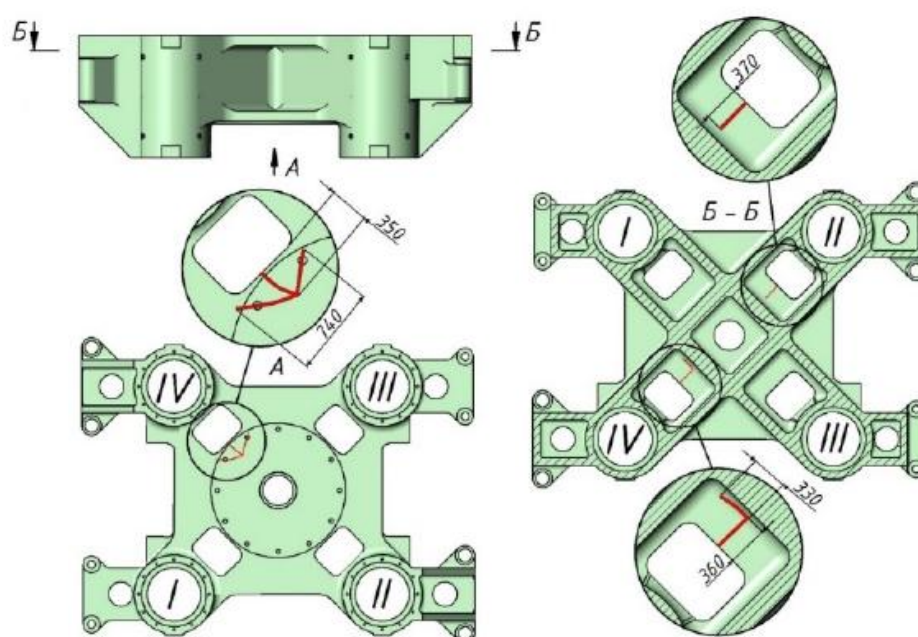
Схема расположения и размеры трещин в корпусе подвижной траверсы
